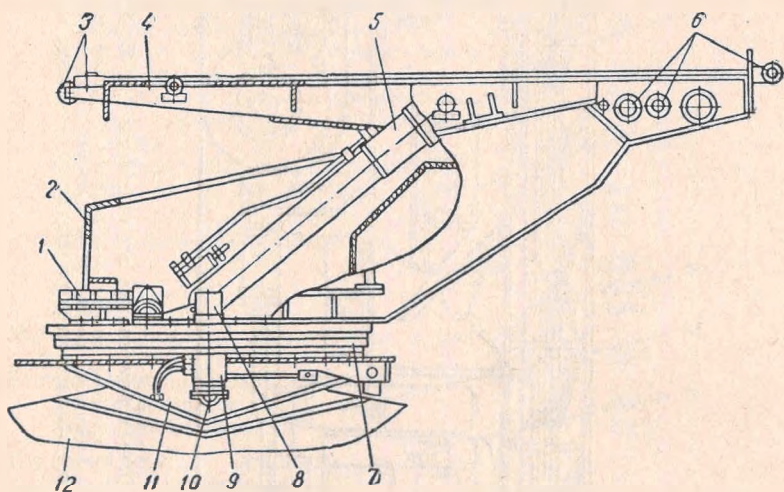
Подъемно-поворотное устройство автолестницы АЛ-45(257), ПМ-109:
